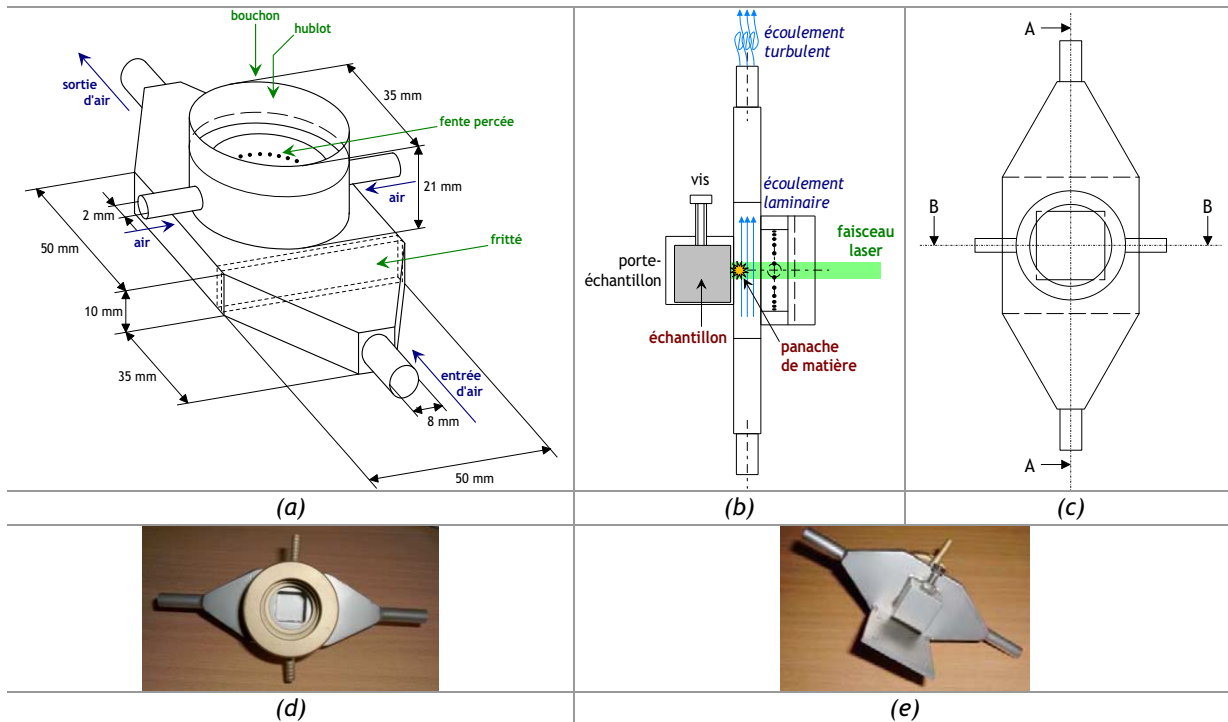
Cellule d'ablation en acier inoxydable : vue en 3 dimensions (a), vue en 2 dimensions de profil (b) et du dessus (c), photo de la face avant (d) et de la face arrière (e)
